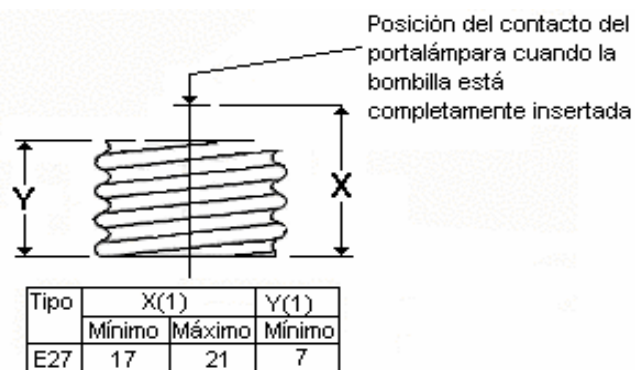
Dimensiones del casquillo de una bombilla en mm.
